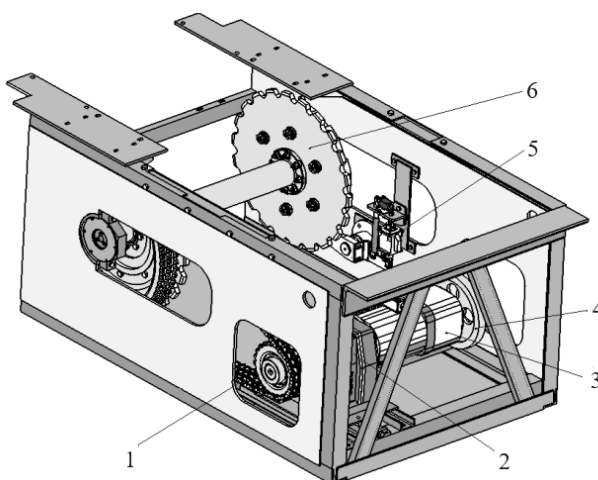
Конструктивное исполнение привода эскалатора ЭС04К:
